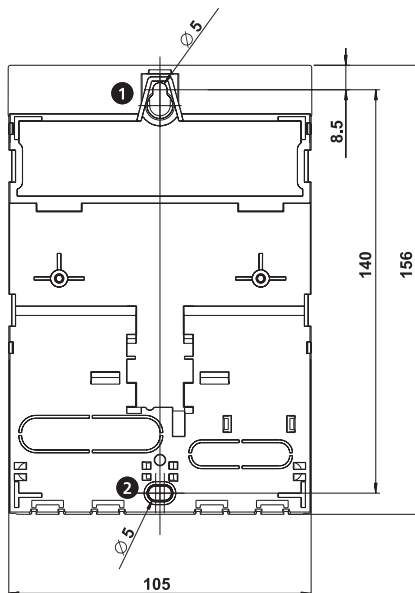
Rückseite des Reglers mit Montageöffnungen oben ❶ und unten ❷
